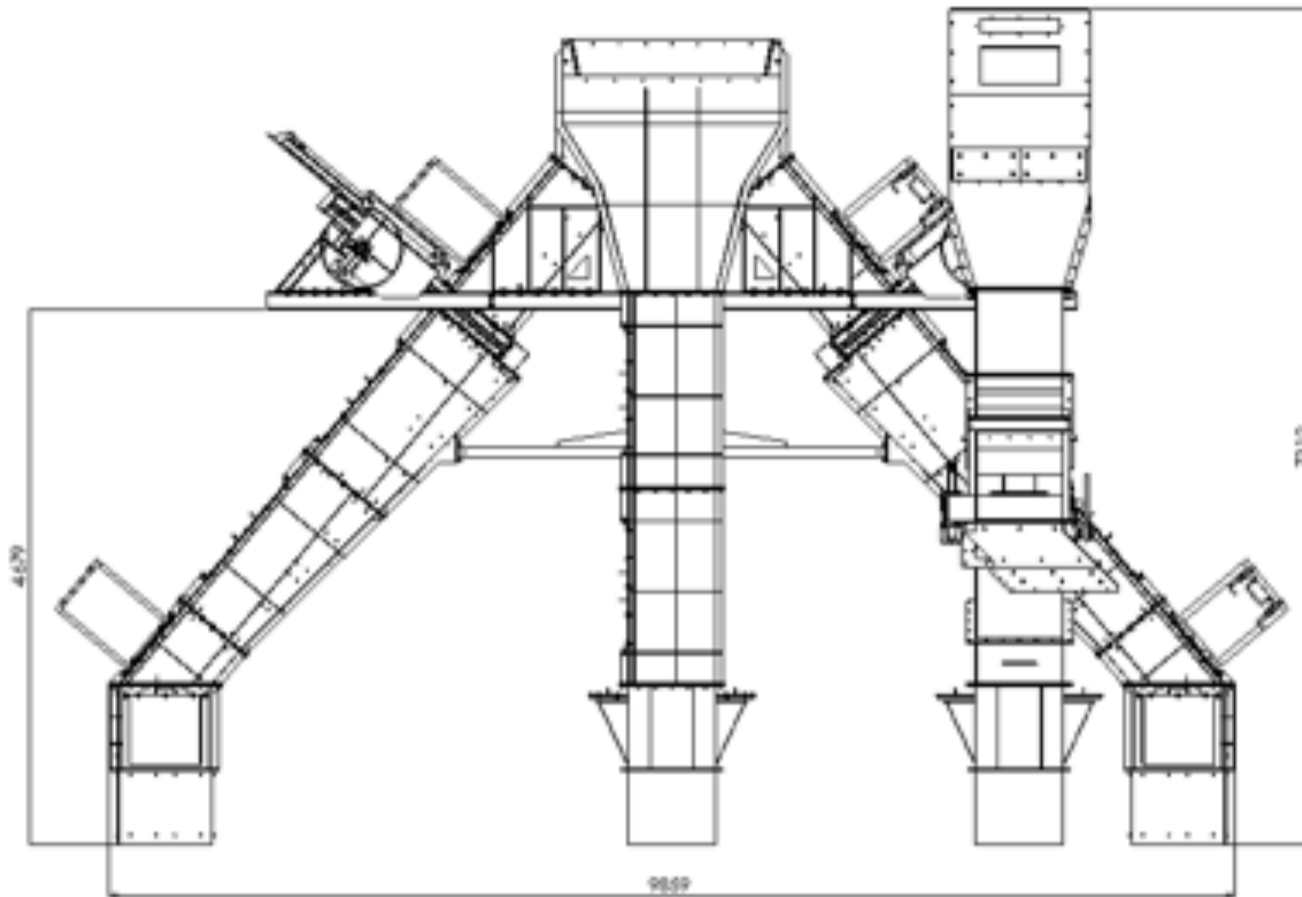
Widok jednej sekcji zaprojektowanej konstrukcji zabudowy podajników i przesiewaczy wibracyjnych - rzut wymiarów gabarytowych
